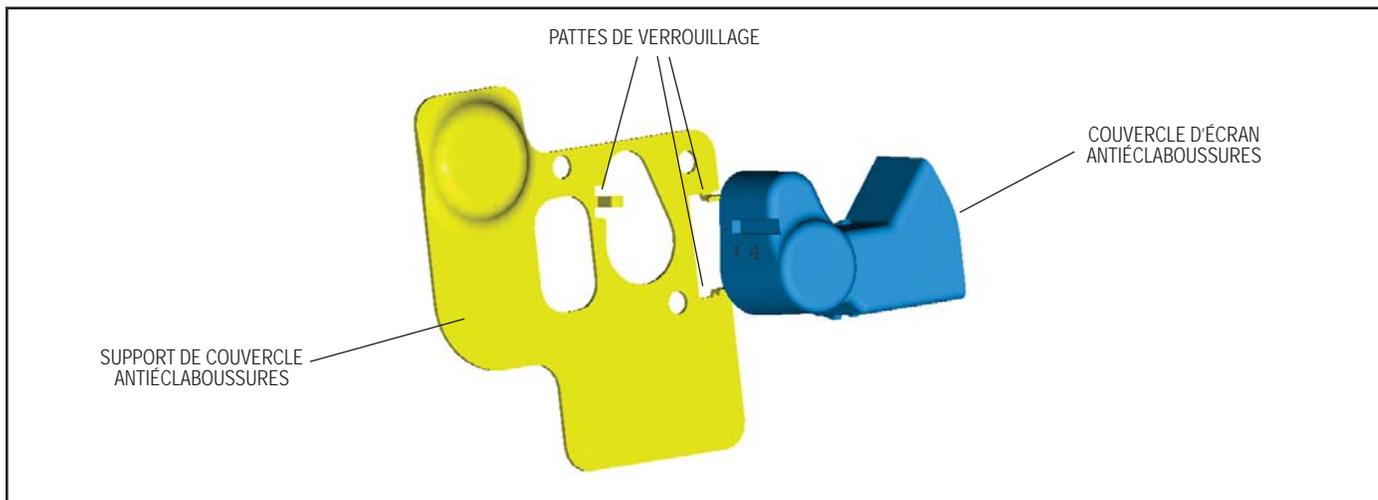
SUPPORT ET COUVERCLE ANTIÉCLABOUSSURES – (VUE ÉCLATÉE)
